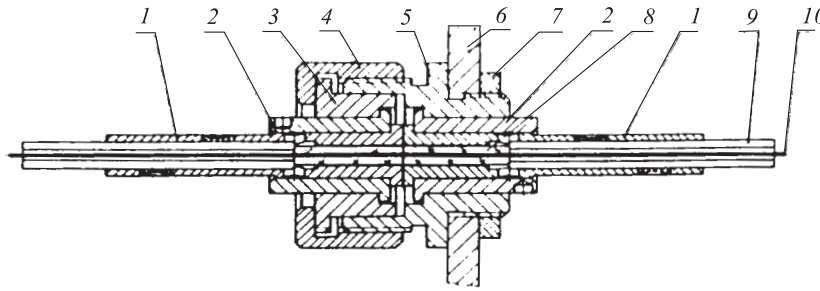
Юстируемый оптический соединитель «кабель — кабель»: 1 — хвостовик; 2 — втулка эксцентриковая; 3 — втулка фиксирующая; 4 — накладная гайка; 5 — корпус гильзы; 6 — панель прибора; 7 — гайка крепежная; 8 — капилляр; 9 — оболочка волоконно-оптического кабеля; 10 — световод
